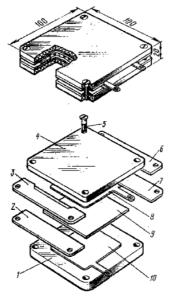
Внешний вид и деталировка элемента, вырабатывающего озон
